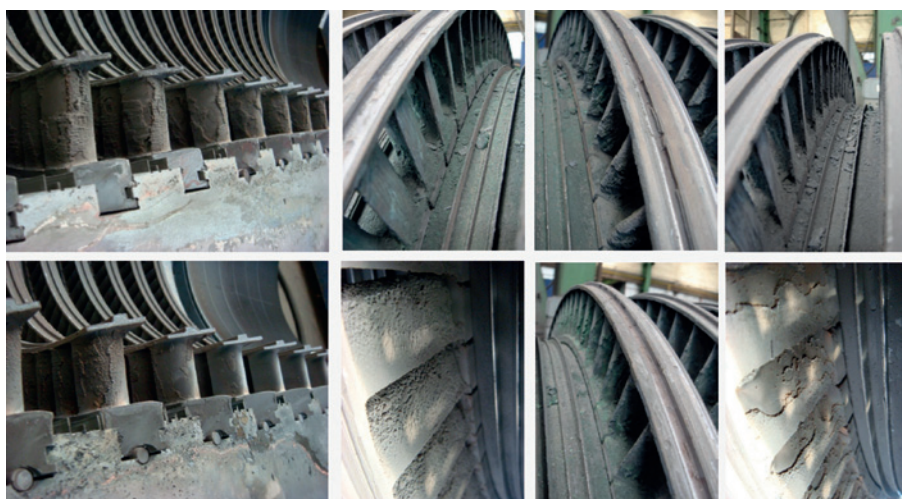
Przykład korozji postojowej i degradacji materiału łopatek wirnikowych (a) oraz tarczy wirnikowej (b)
